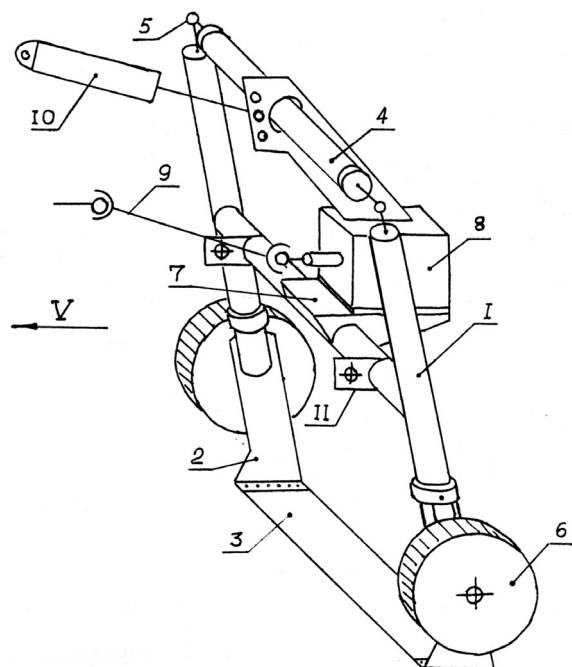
Подрезчик корней горизонтальный для лесных питомников: 1 – рама; 2 – черенок; 3 – нож; 4 – стяжка; 5 – шарнир; 6 – опорное колесо; 7 – плита; 8 – вибратор; 9 – соединительный вал; 10 – регулятор угла резания; 11 – кронштейн навески
